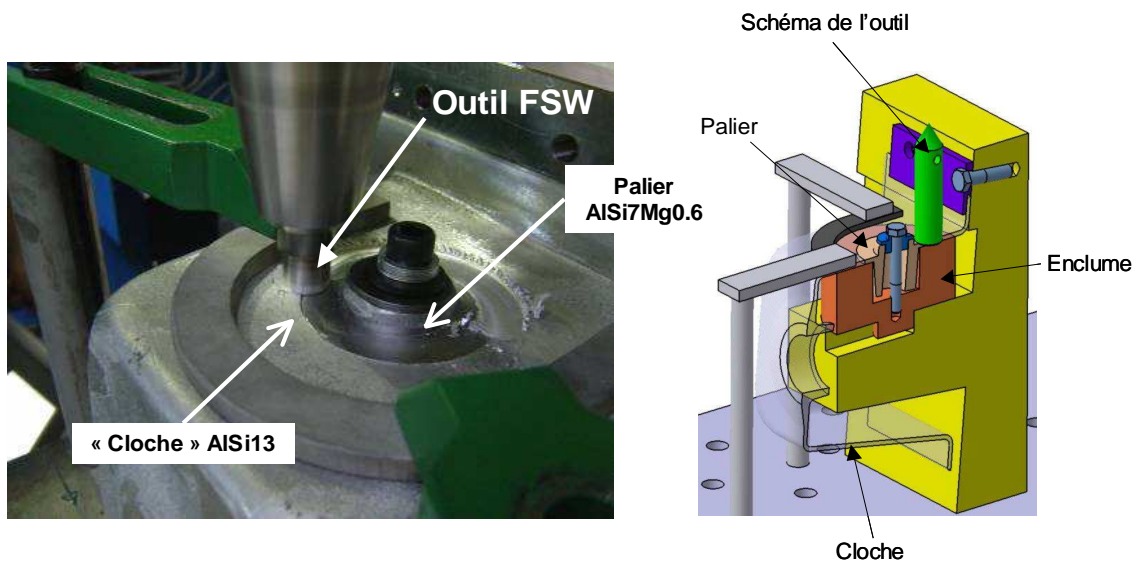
montage pour le soudage du palier latéral sur la cloche.
